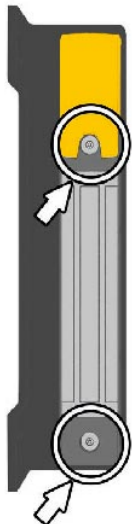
Prozesszuhaltung auf Montageplatte anbringen und Schrauben M6 x 25 mm Torx festziehen.
